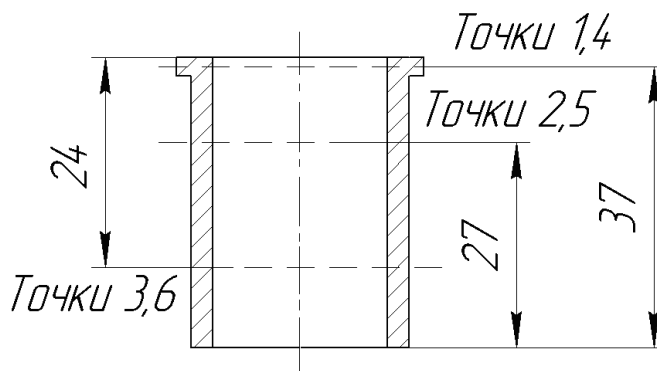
Схема расположения контрольных точек на рабочей поверхности гильзы цилиндра.
